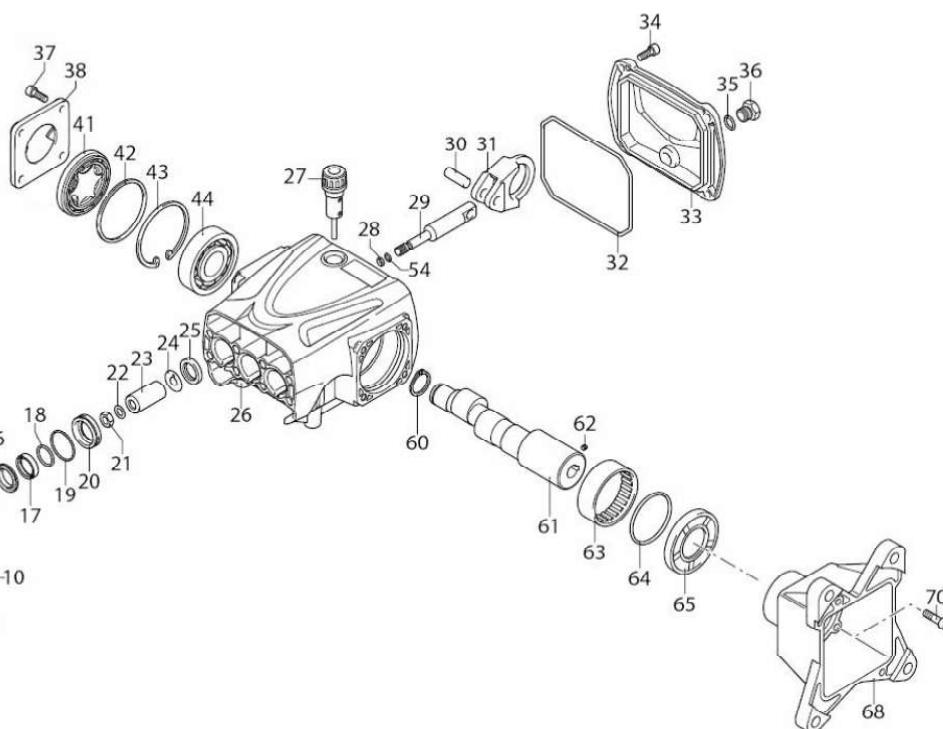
Illustration des pièces de réparation 3-0390 082919
